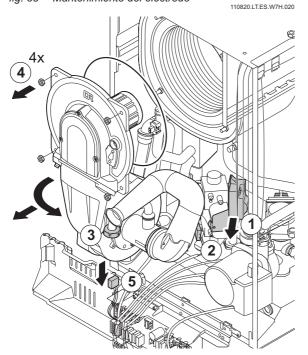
Cómo desmontar la placa frontal del intercambiador de calor
